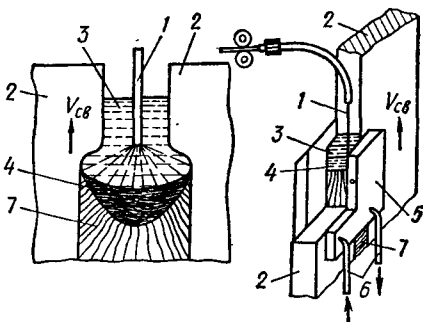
Схема процесса электрошлаковой сварки
